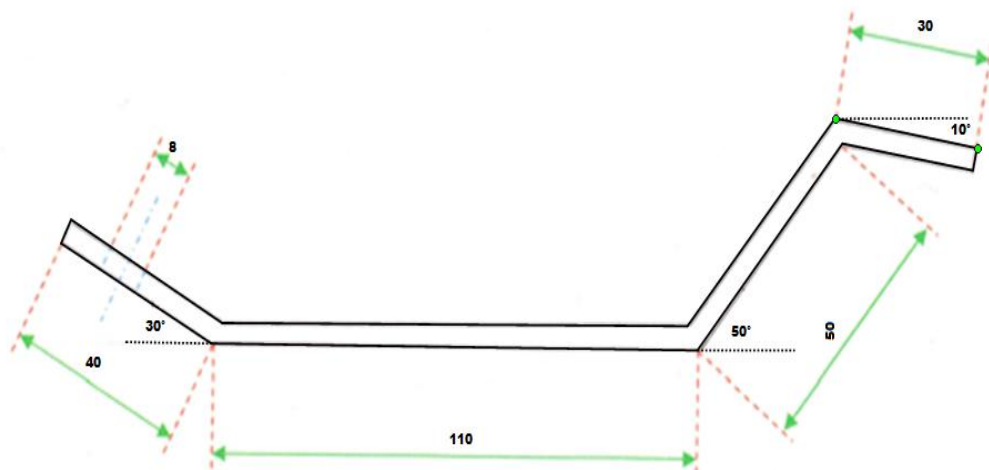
Plano de las extensiones posteriores de los enganches de hebillas
